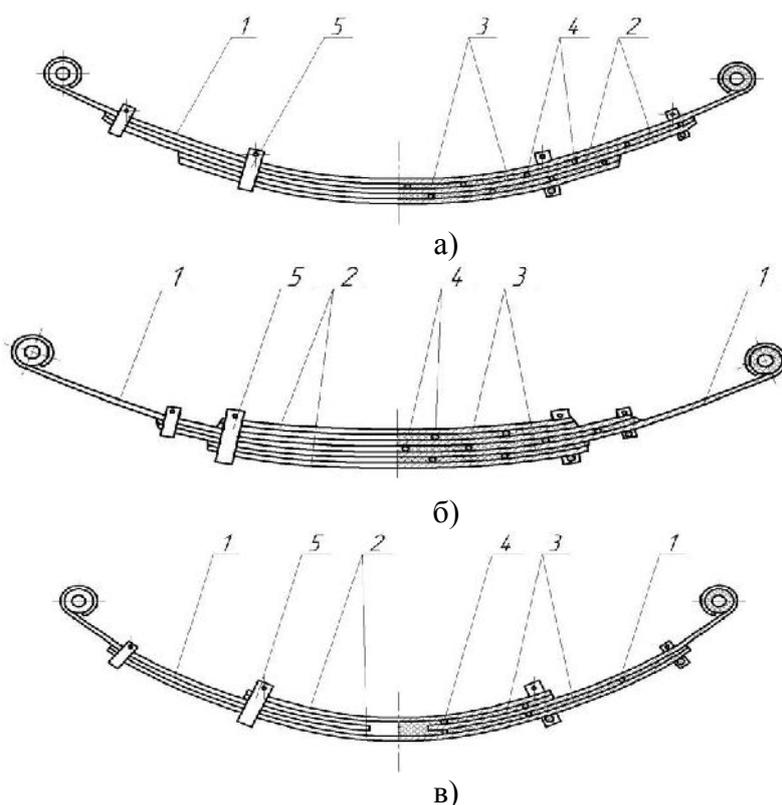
Варианты конструктивных решений рессоры с упруго-вязкими слоями:
